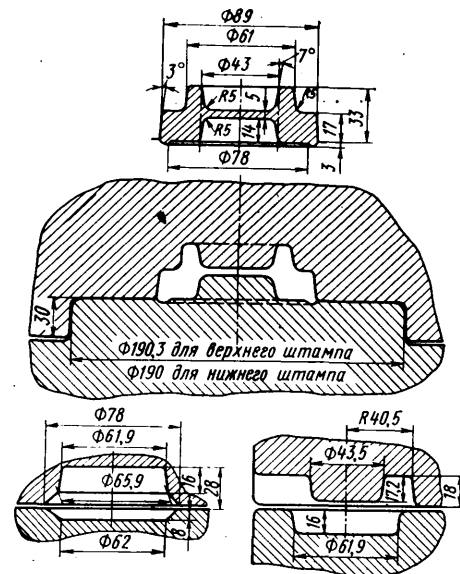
Поковка (верхняя часть чертежа) и конструкция молотового штампа (первый вариант) со специальными высадочным и осадочным ручьями
